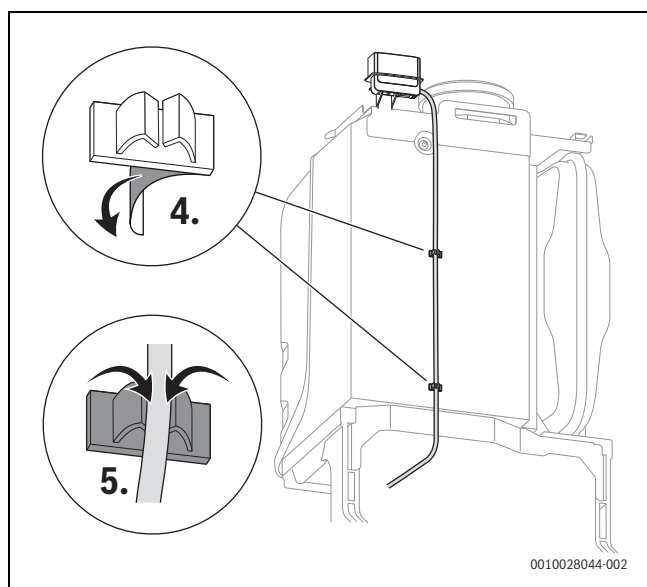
Montarea suportului pentru cabluri pe partea posterioară a aparatului și fixarea cablului
